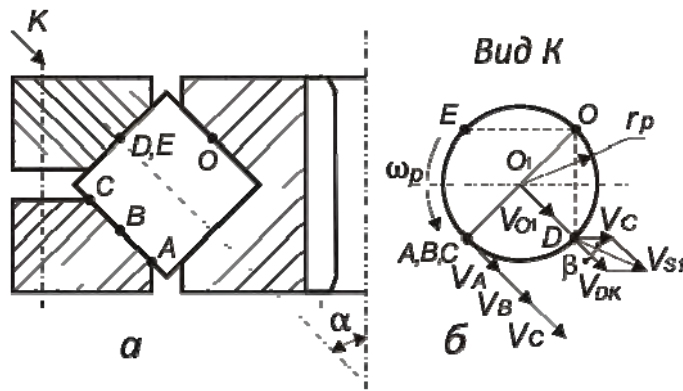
Частина конструкції опорно-поворотного пристрою:
